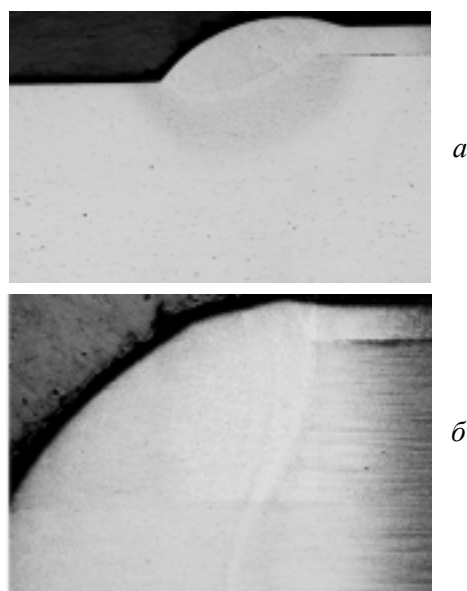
Сталь ЭК-181. Микроструктура (металлография) сварных соединений (рис. 16) трубчатых образцов диам.6,9×0,4 мм (увеличение ×15, нетравленое состояние): а – сварное соединение, выполненное дугой, управляемой магнитным полем (ДУМП); б – периметрическое сварное соединение
